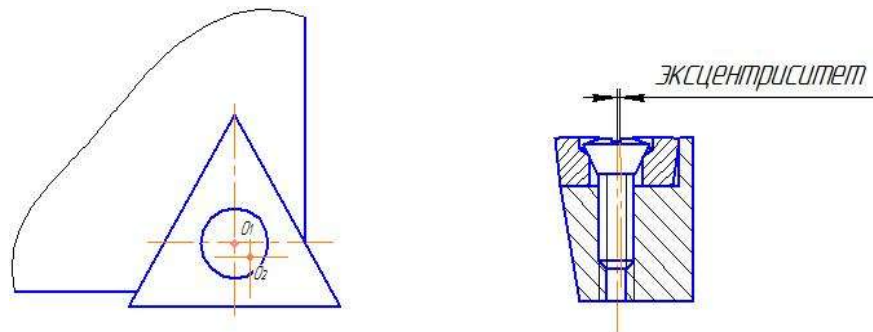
Узел крепления пластины в резцовой вставке
